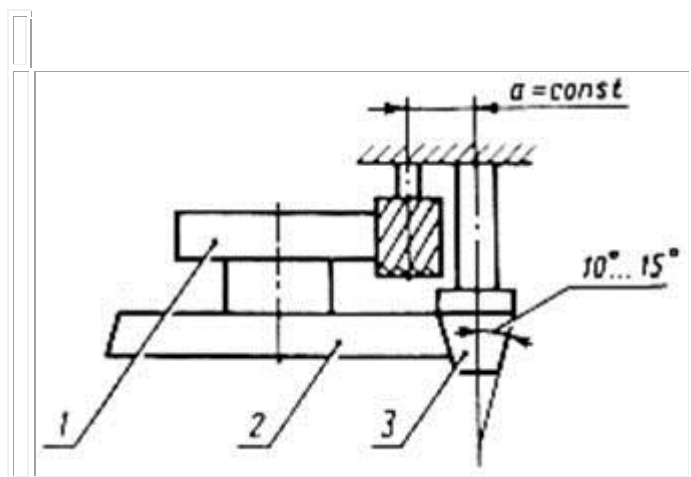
Схема копировального устройства при работе по копиру (1 - заготовка; 2 - копир; 3 - ролик).
